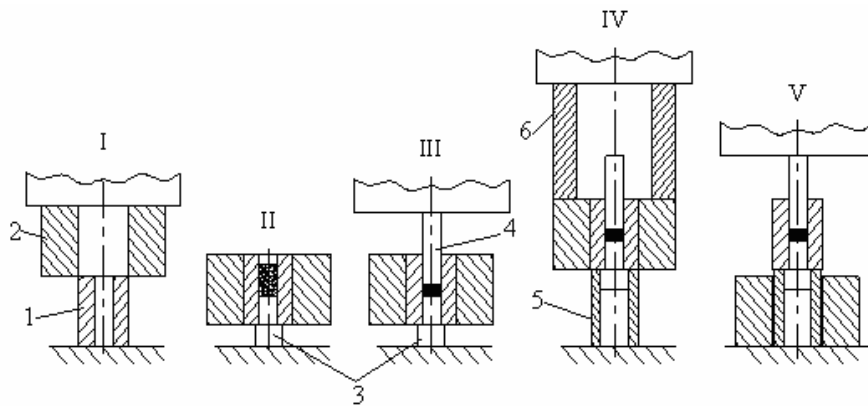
Этапы цикла прессования порошковых материалов в пресс-форме с взаимноцилиндрическими контактными поверхностями матрицы и бандажа: I – запрессовка матрицы в бандаж; II – засыпка порошка в матрицу; III – прессование; IV – снятие бандажа с матрицы; V – выпрессовка; 1 – матрица; 2 – бандаж; 3 – пуансон нижний; 4 – пуансон верхний; 5, 6 – втулки
